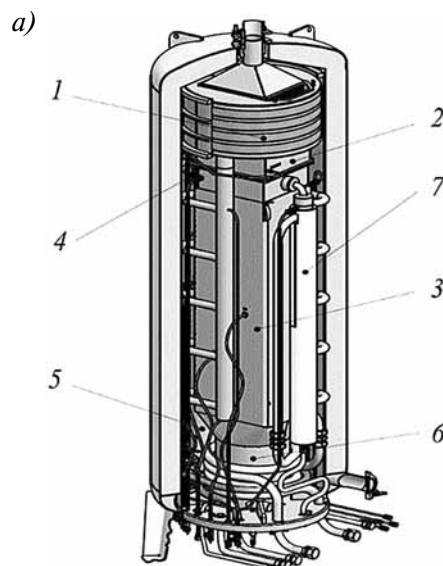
Моноблочный конвертор филиала ЦНИИ СЭТ:
